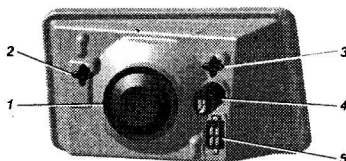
Корпус фары автомобилей ГАЗ-3102, ГАЗ-310221, ГАЗ-310231:
